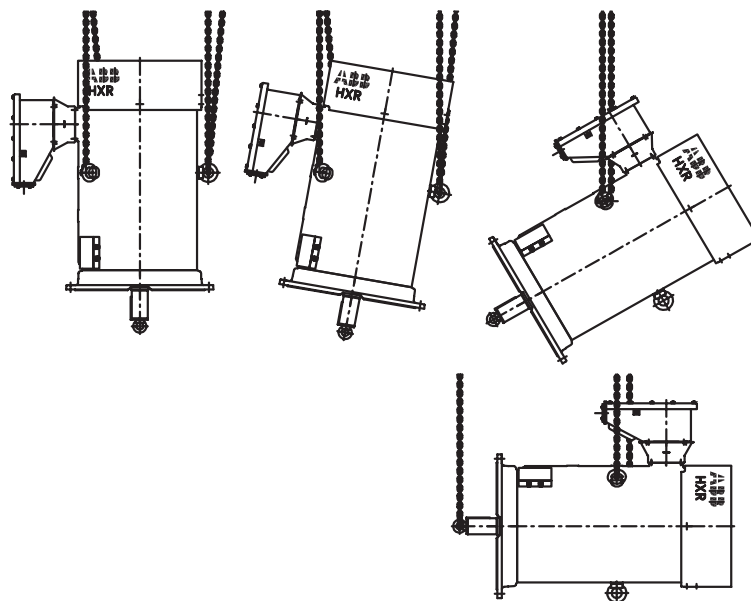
Machine équipée d'anneaux de levage tournants : levage et rotation
